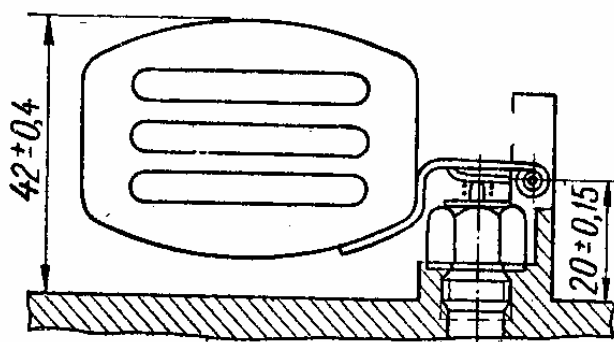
Схема розміщення поплавка в карбюраторі К-135МУ
